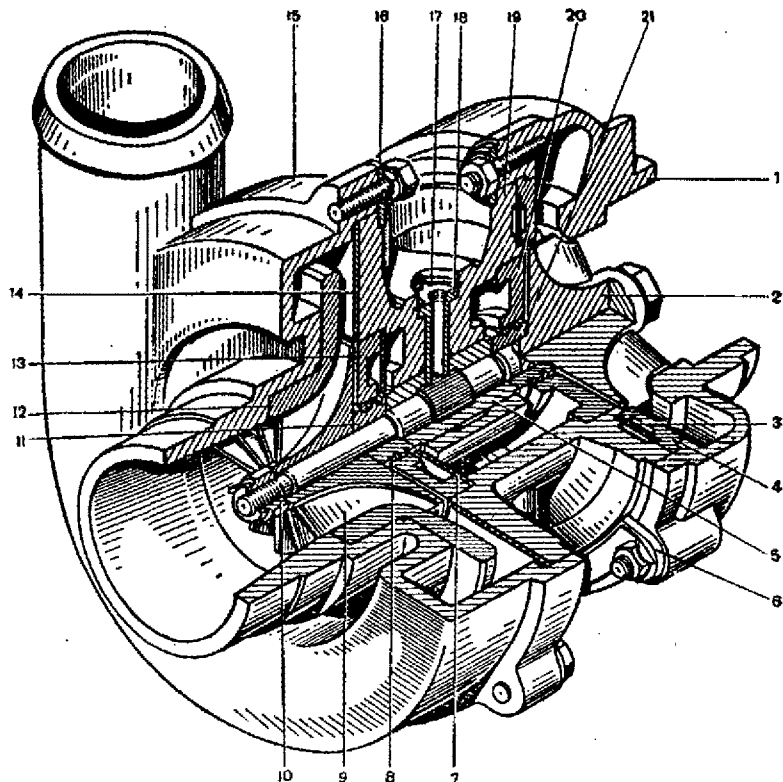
Турбокомпрессор ТКР-7Н-6: 1 – корпус турбины; 2 – колесо турбины с валом; 3 – прокладка; 4 – диск турбины; 5 – подшипник; 6 – планка пружины; 7 – маслоотражатель; 8 – кольцо уплотнительное; 9 – колесо компрессора; 10 – гайка; 11 – втулка; 12 – диффузор; 13, 14, 20 – диски; 15 – корпус компрессора; 16 – шайба прижимная; 17 – кольцо стопорное; 18 – фиксатор; 19 – корпус средний; 21 – втулка
